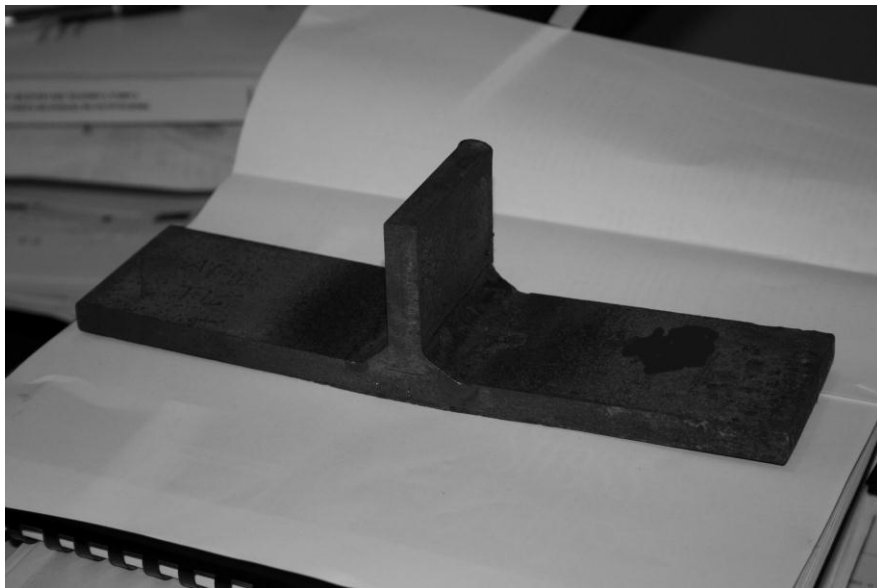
Junta “T” – provete como soldado.
